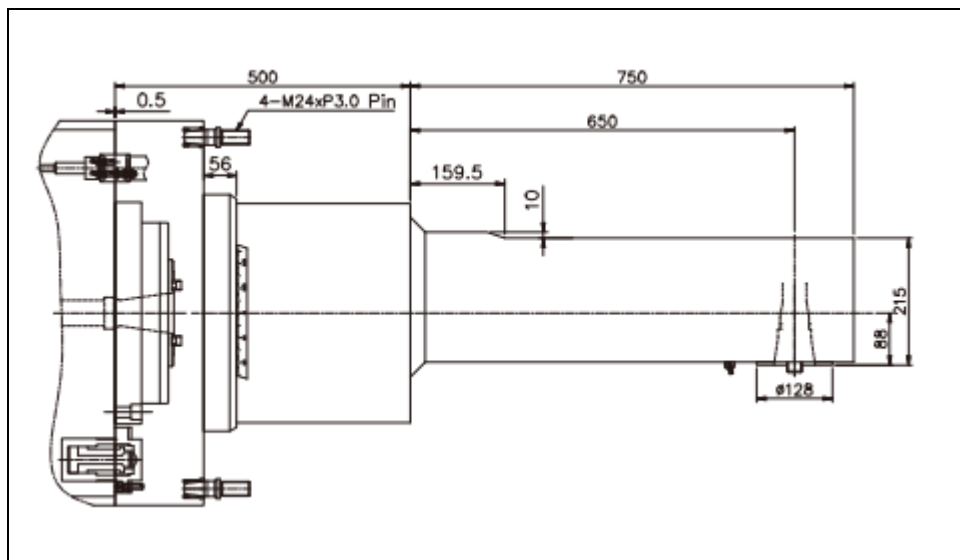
Prodloužená frézovací hlava TM1 EX HT [22]
